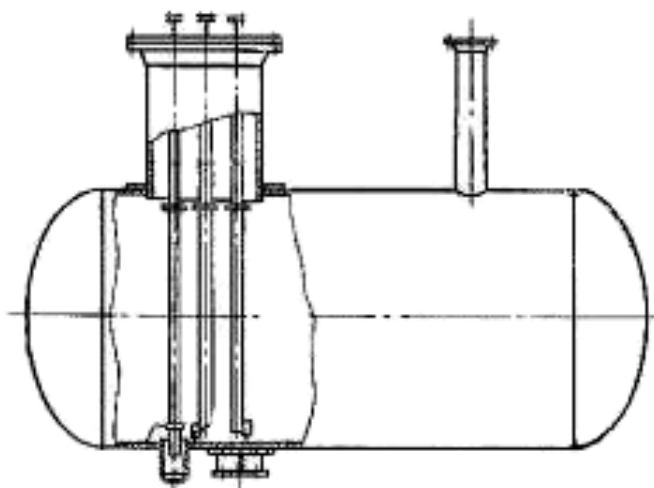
Общий вид эскиза резервуара РГС-10
